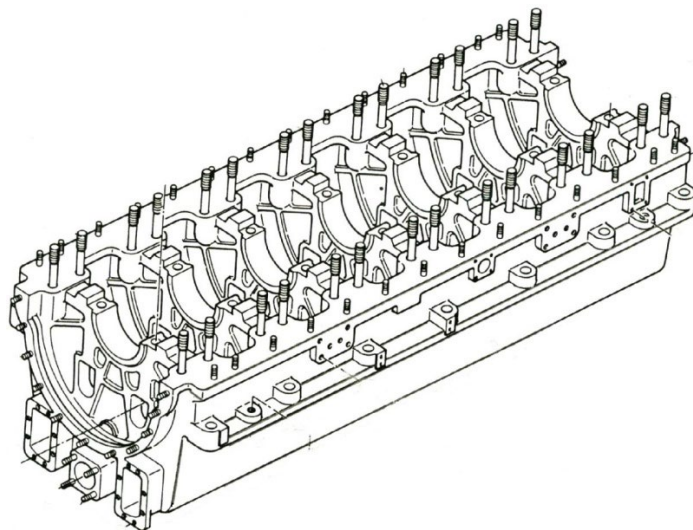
Фундаментна рама MAN B&W MC-C
